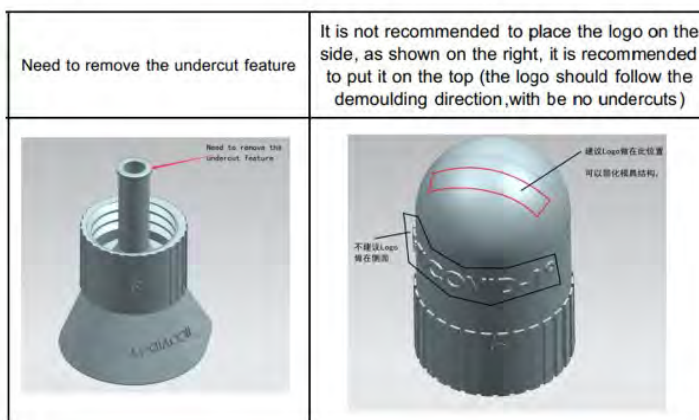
Detalle de análisis de costo de producción de partes del dispositivo de colecta de saliva y cambios necesarios en el diseño para la manufactura del molde de inyección. Fuente: KEMAL Precision Manufacturing.
